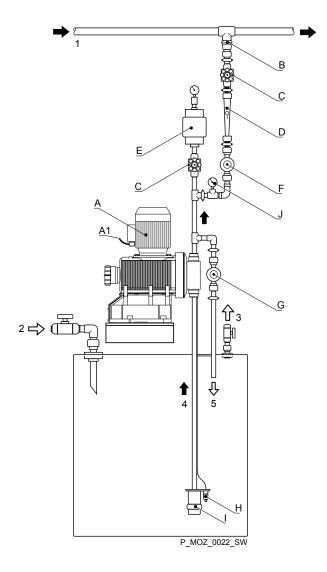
Instalação padrão bomba de dosagem de motor e componentes da instalação, ver tabela seguinte
